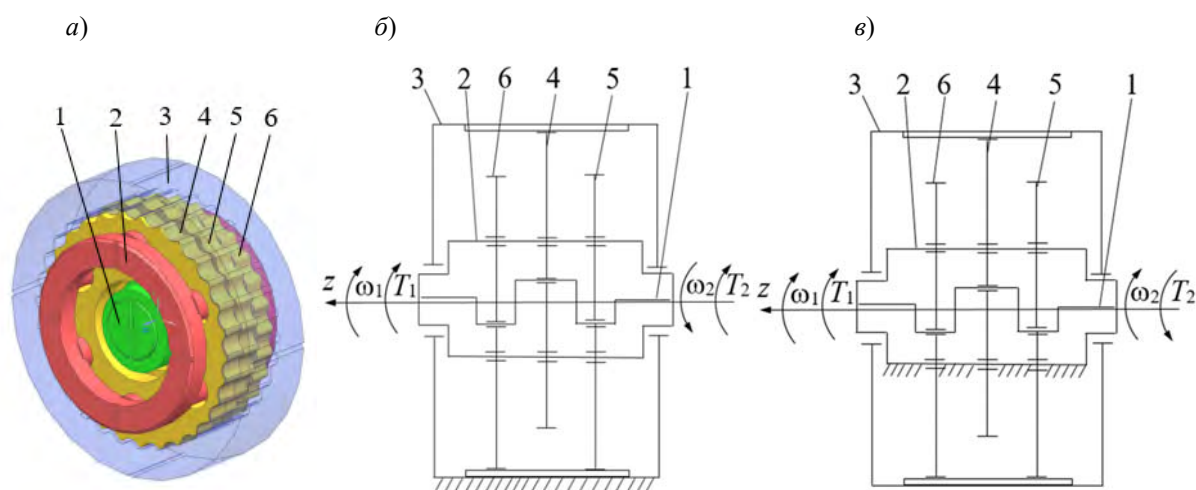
Общий вид (а) и кинематические схемы компьютерных моделей циклоидально-цевочной передачи с остановленным центральным колесом (б) и остановленным механизмом параллельных кривошипов (в): 1 – ведущий вал; 2 – вал с пальцами; 3 – цевочное колесо; 4–6 – сателлиты
